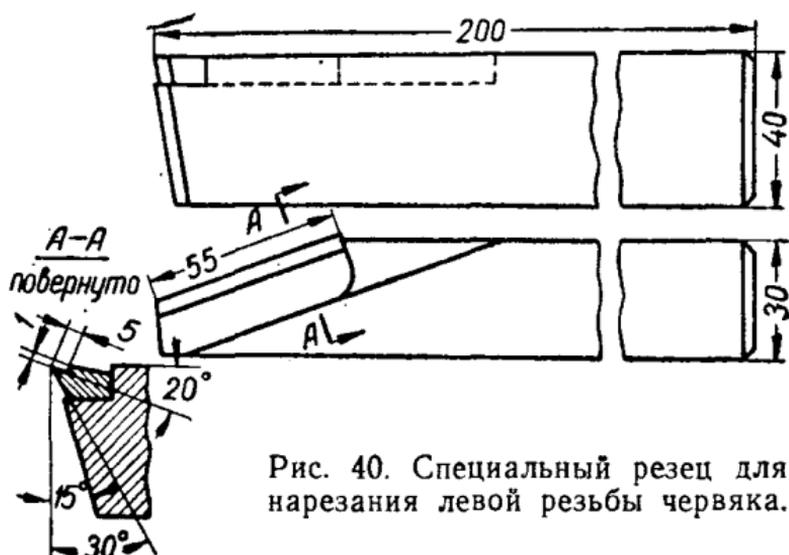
Специальный резец для нарезания левой резьбы червяка.
